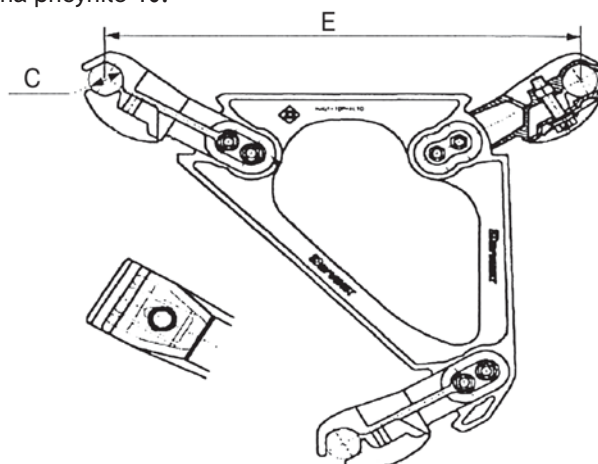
Внешний вид амортизирующих распорок ENxx-3Xxxx(BA)(R)
